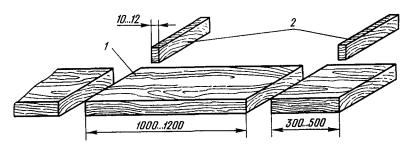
Схема выпиловки контрольного образца: 1—контрольный образец, 2—секции влажности
